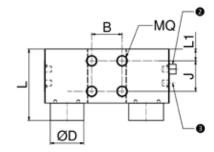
Passive pneumatische Klemmelemente für Standard-Linearführungen
